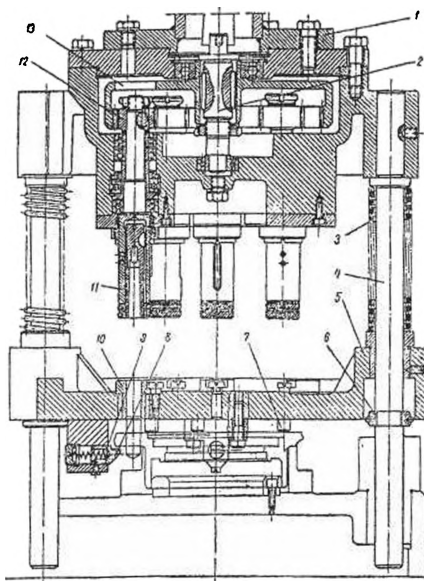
Головка з кондукторною плитою і направляючими втулками
